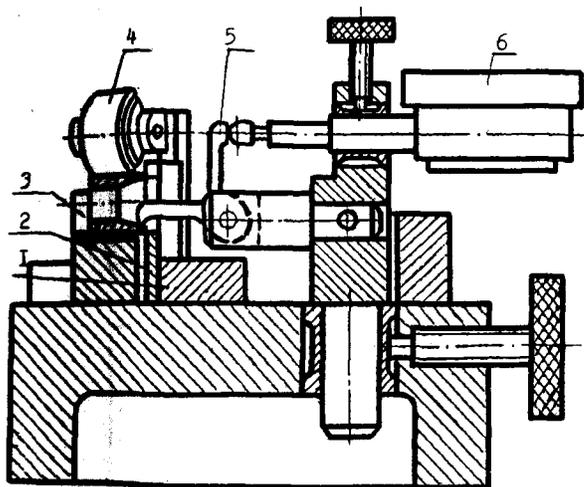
Приспособление для контроля угла в дисках с конусным отверстием:
